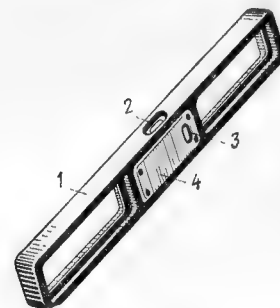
1 — корпус; 2 — ампула, 3 — винт; 4 — крышка
